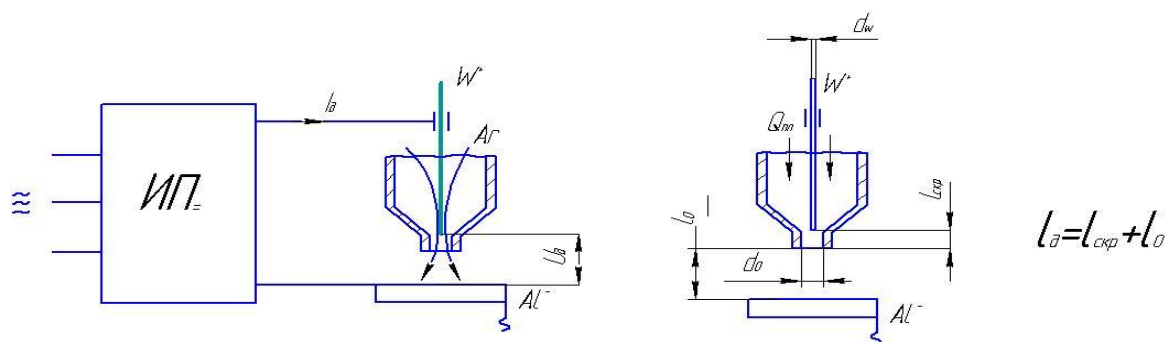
Схема сварки сжатой дугой неплавящимся электродом
